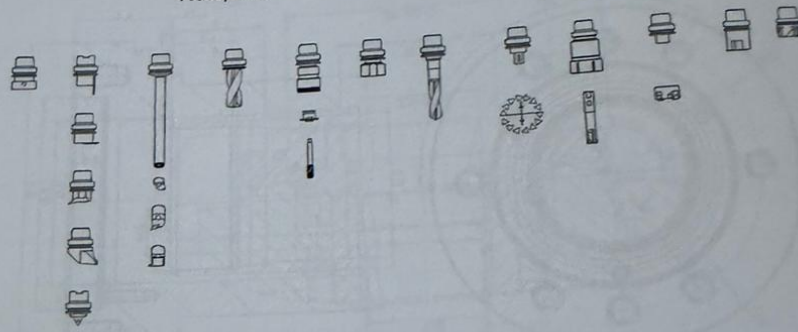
werkzeugsystem_fraesspindel.CGM
